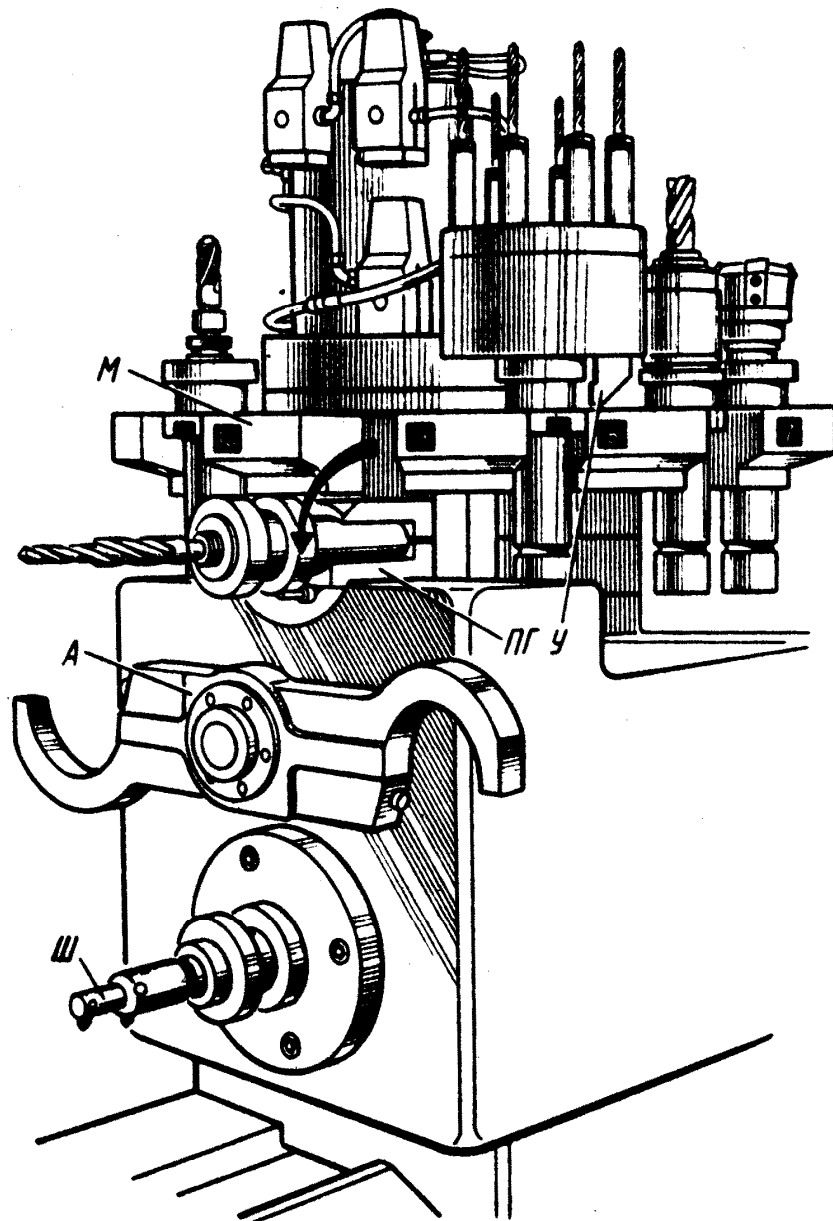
Інструментальний магазин для окремих інструментів і багатошпindelних головок з пристроєм АЗІ
